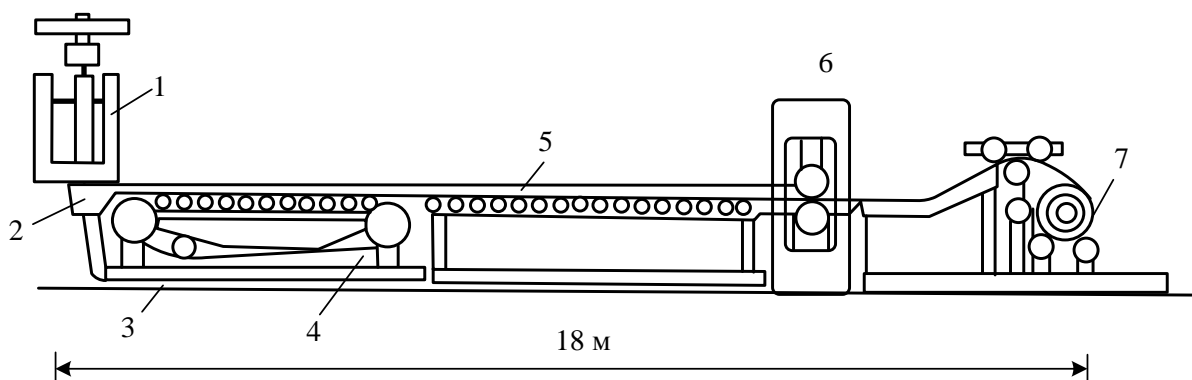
Схема установки «Клаусталь II» для отливки полосы: 1 – печь; 2 – разливочное устройство; 3 – натяжной ролик; 4 – водяная камера; 5 – холодильник; 6 – прокатная клетка; 7 – моталка
